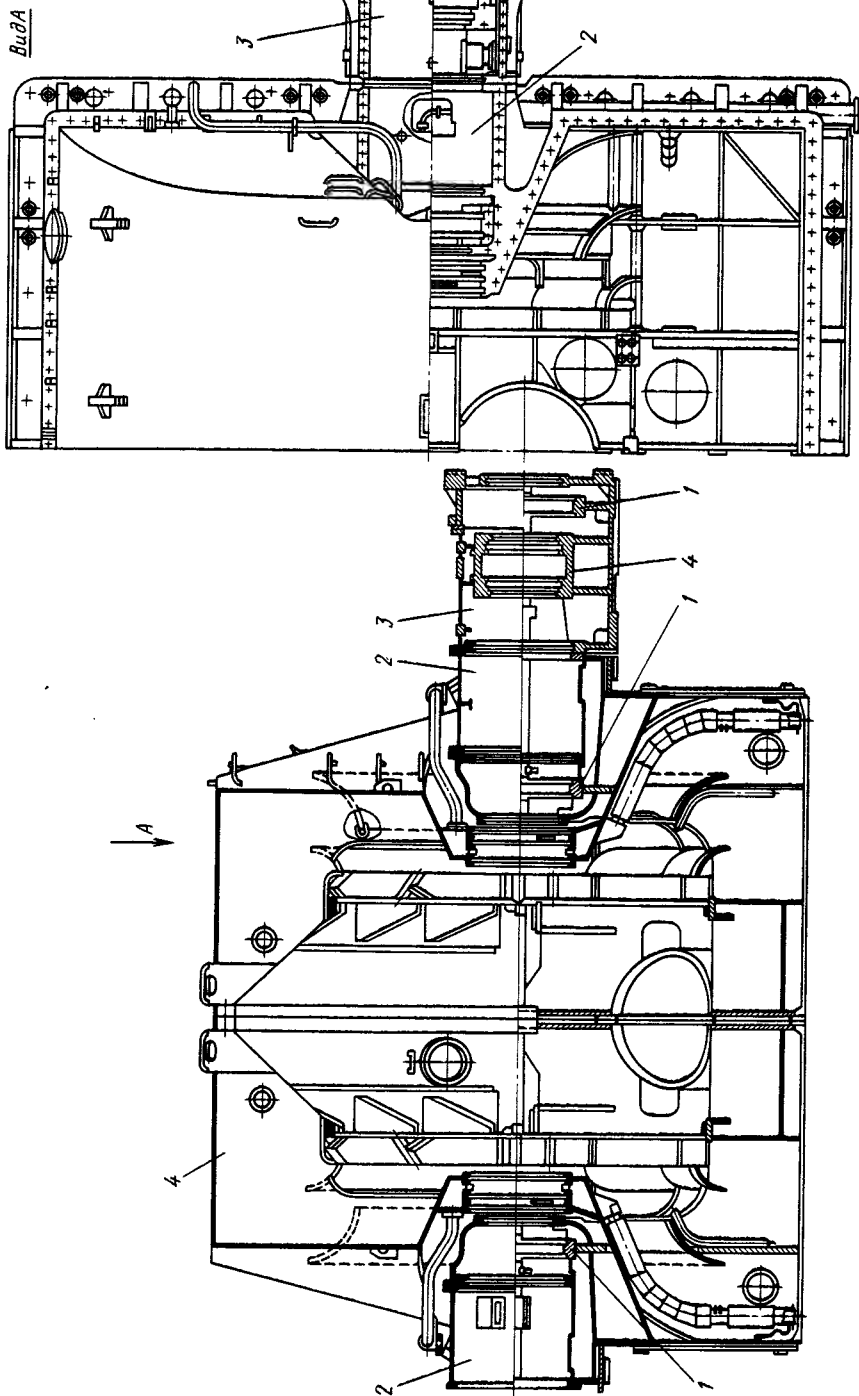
Корпус ЦНД3 турбины К-500-65/3000 ХТЗ со встроенными опорными подшипниками и с приставным корпусом упорного подшипника:
